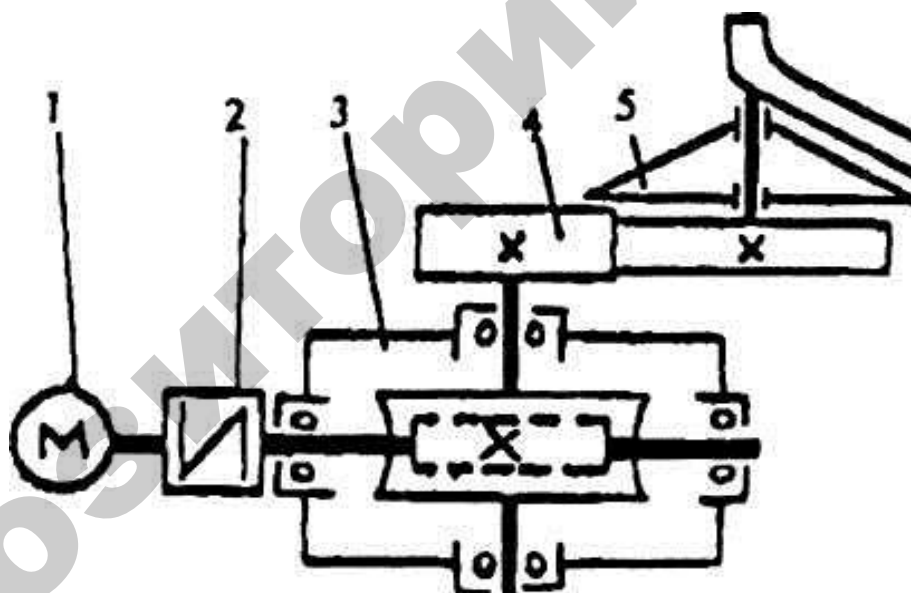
Принципиальная схема привода поворотной трубы автоматизированного элеватора; 1 — электродвигатель; 2 — муфта; 3 — червячный редуктор; 4 — открытая цилиндрическая передача; 5 — поворотная труба
